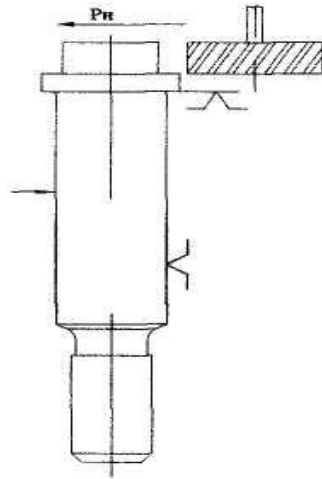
Розрахункова схема сил при фрезеруванні в пристосібленні
